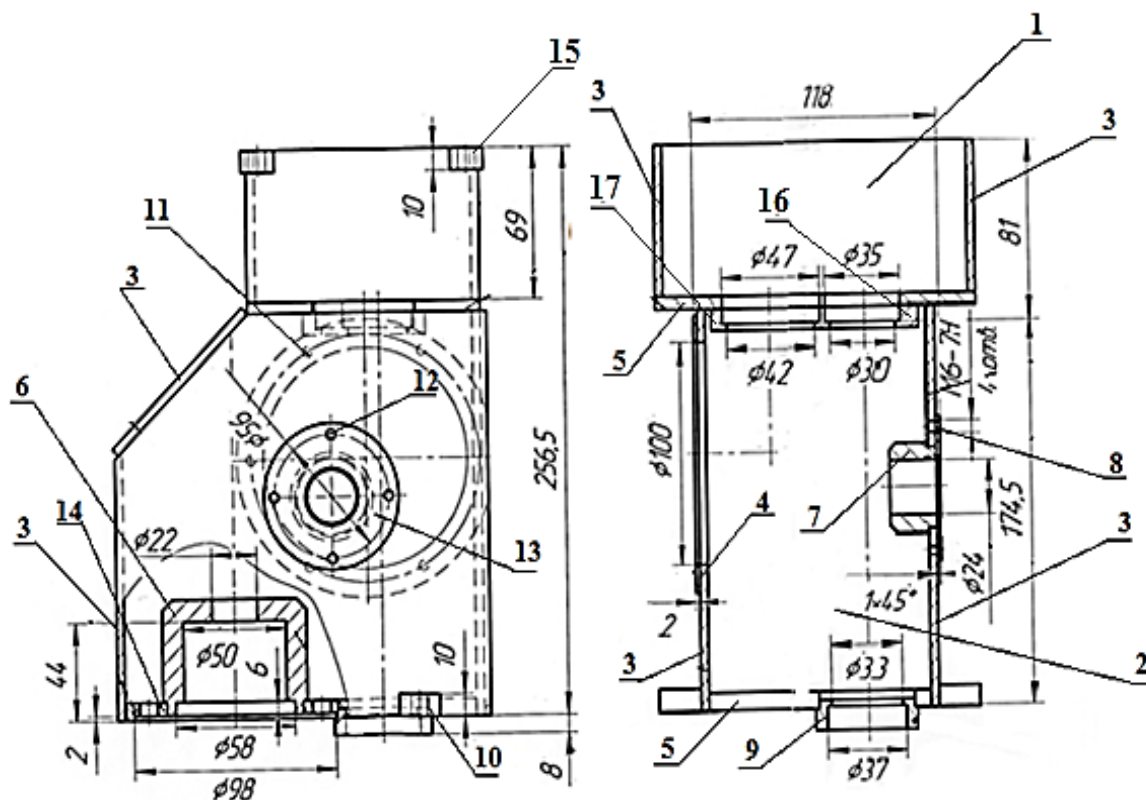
Конструкция основного корпуса перфоратора
